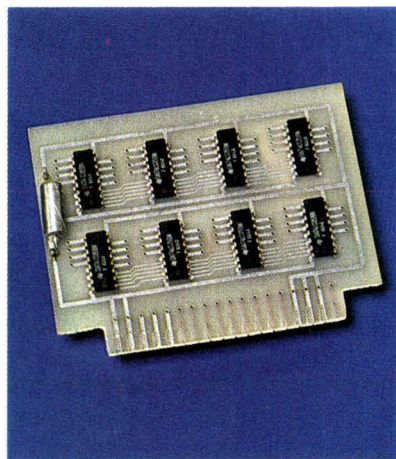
Circuit imprimé vu côté « soudures » d'une carte « fille ».
